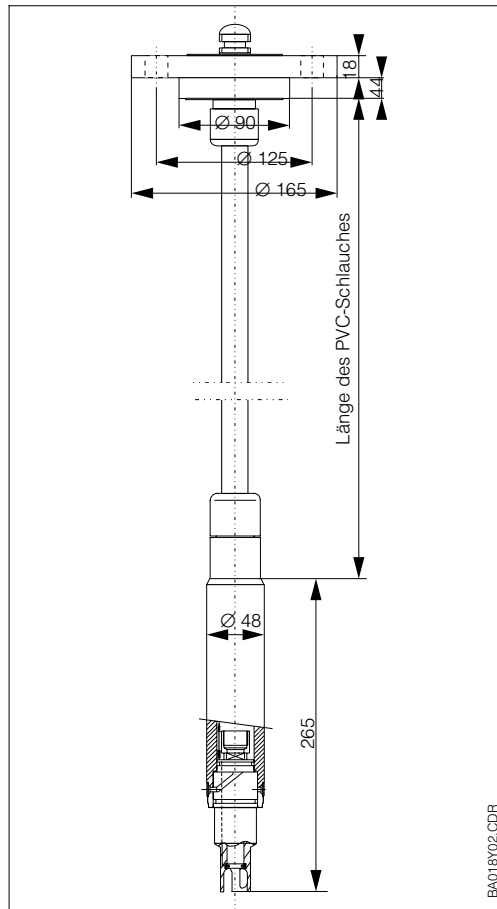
DipFit W CPA 530 mit Flansch DN 50 (links)
